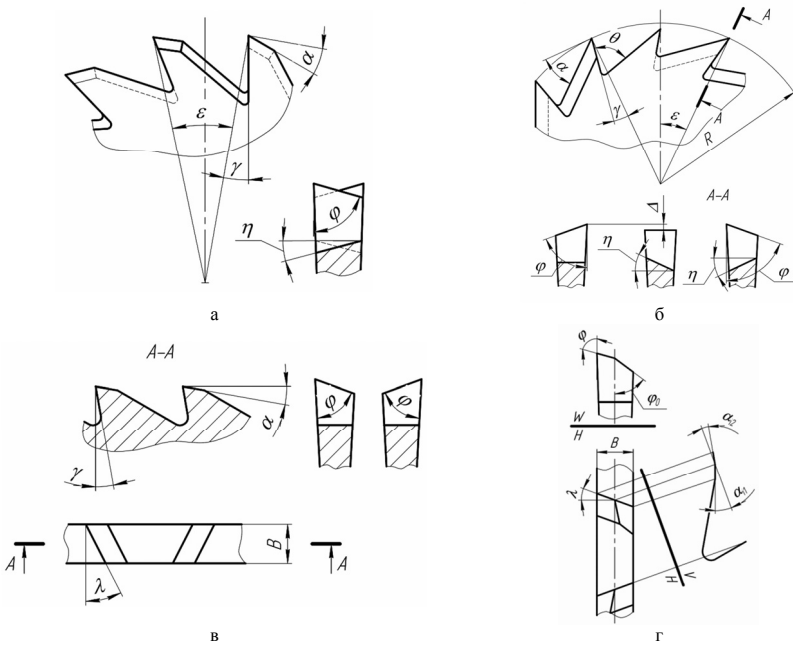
Конструкції різальної частини дискових відрізнних фрез з різнонаправленими зубцями
